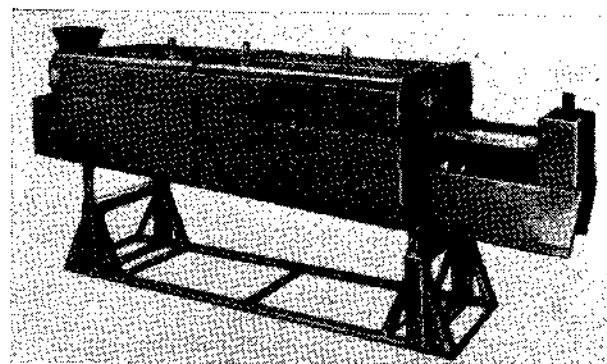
Общий вид трубчатой печи косвенного нагрева для обжига ферритовой шихты
